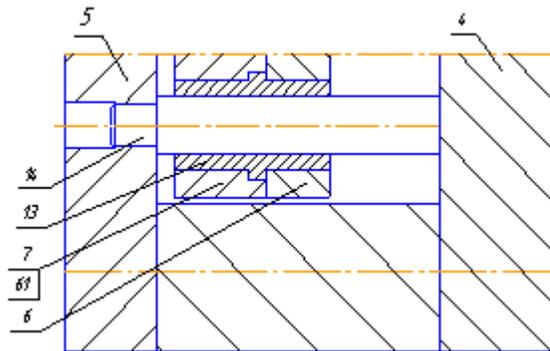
Конструкция колонки направляющей исполнение I: Консоль .
